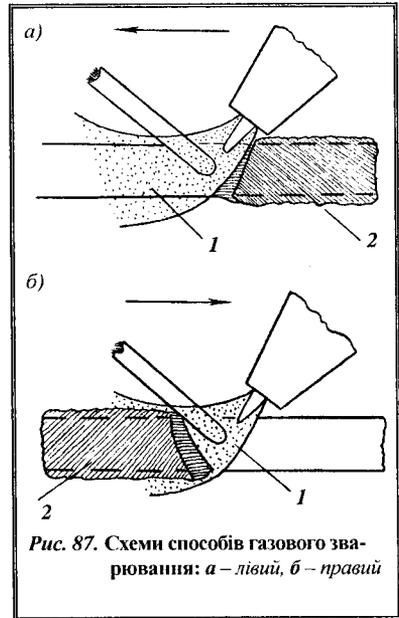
Схеми способів газового зварювання: а – лівий, б – правий
